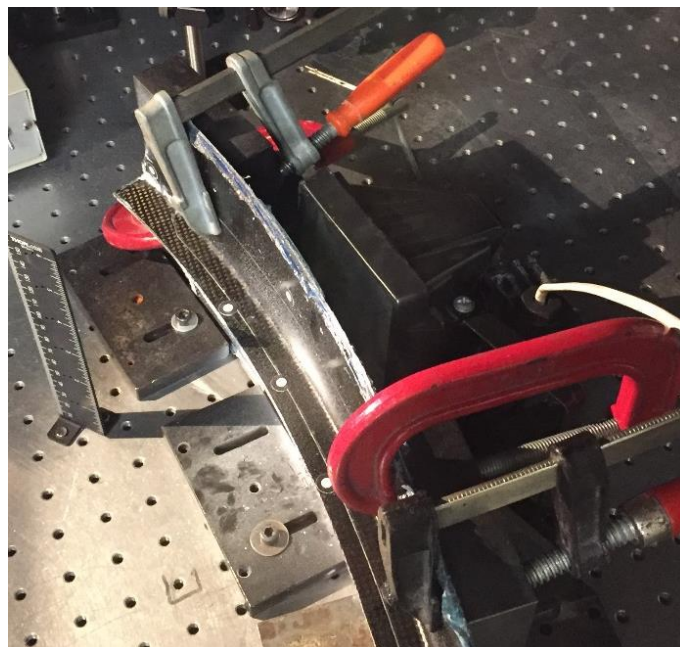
Pormenor da montagem para ensaio da peça.
